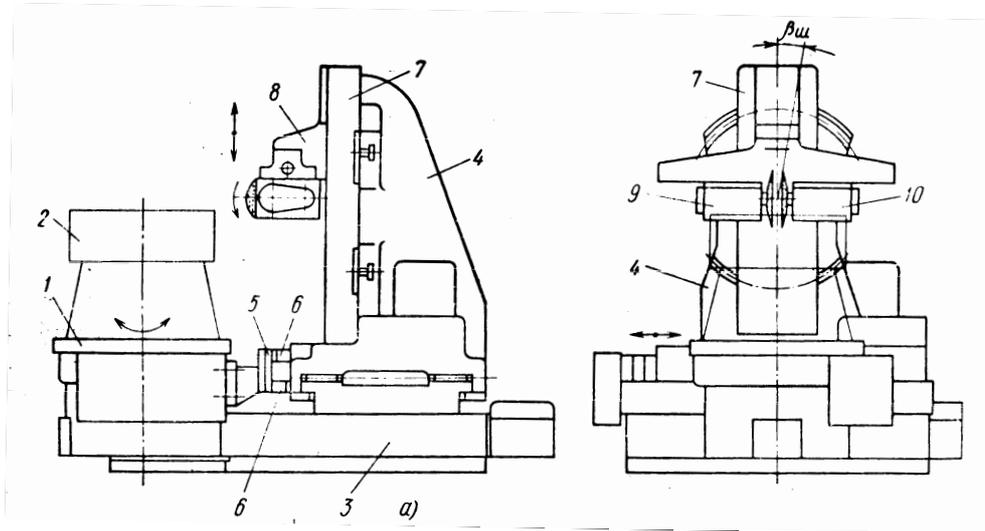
Зубошлифовальный станок для обработки крупномодульных колес:
